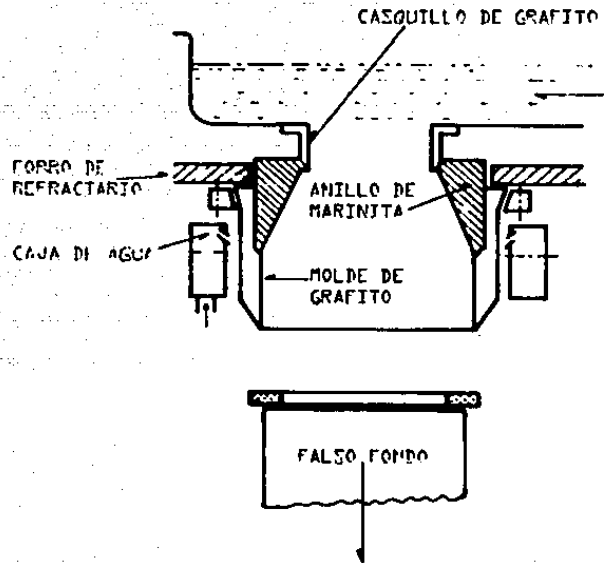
Ensamble Reynolds Mattamould (dibujo esquemático).
